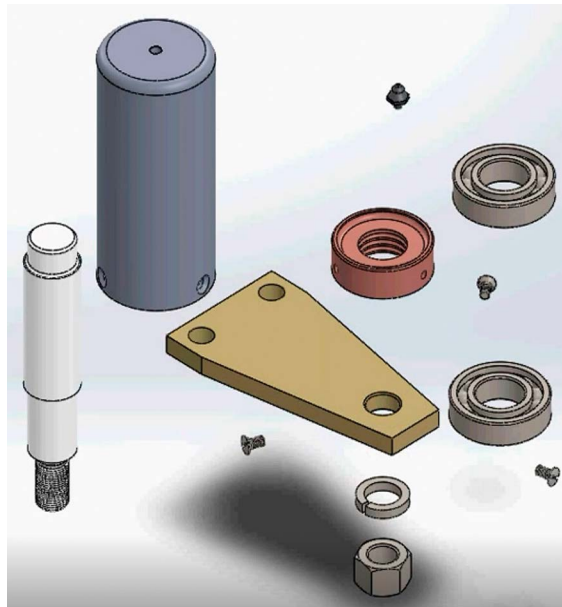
Unidad ensamblada explosionada de rodillo
